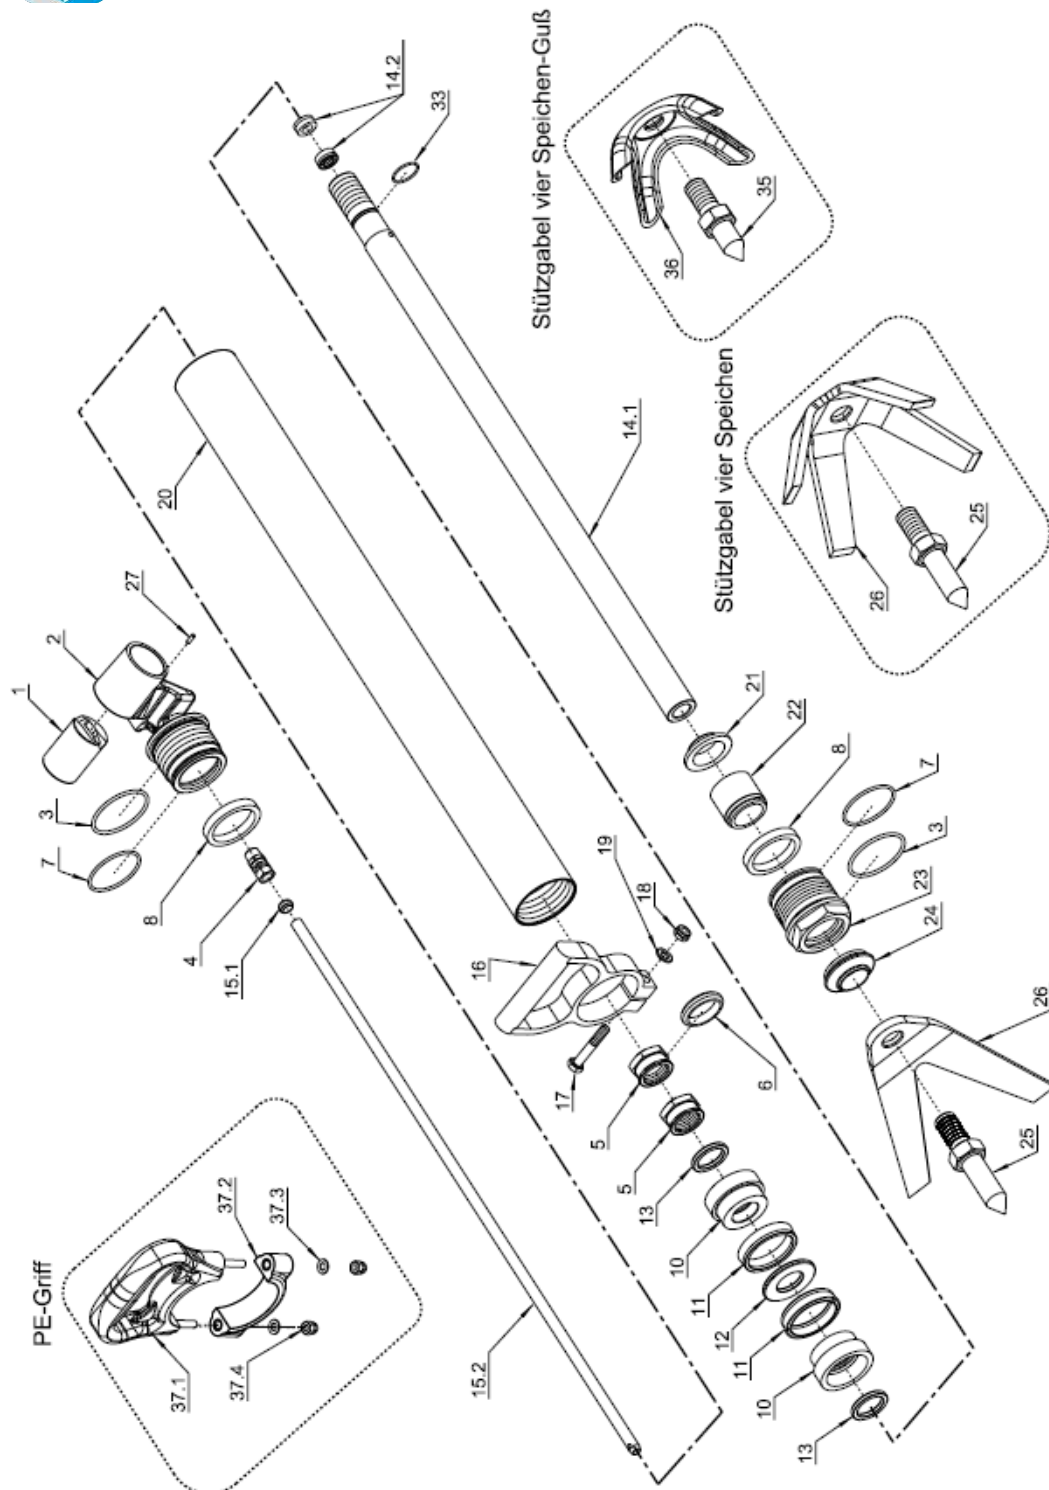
Dispositionszeichnung der Rückzugstütze
